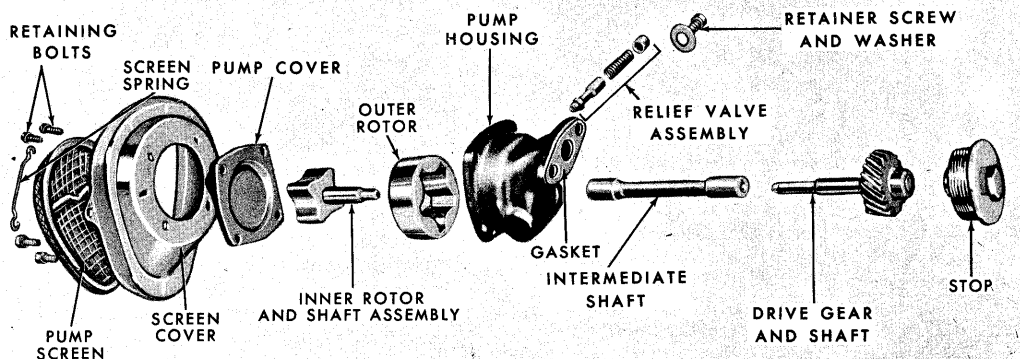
Exploded view af olie pumpen med si, reduktionsventil, aksel og drev.
